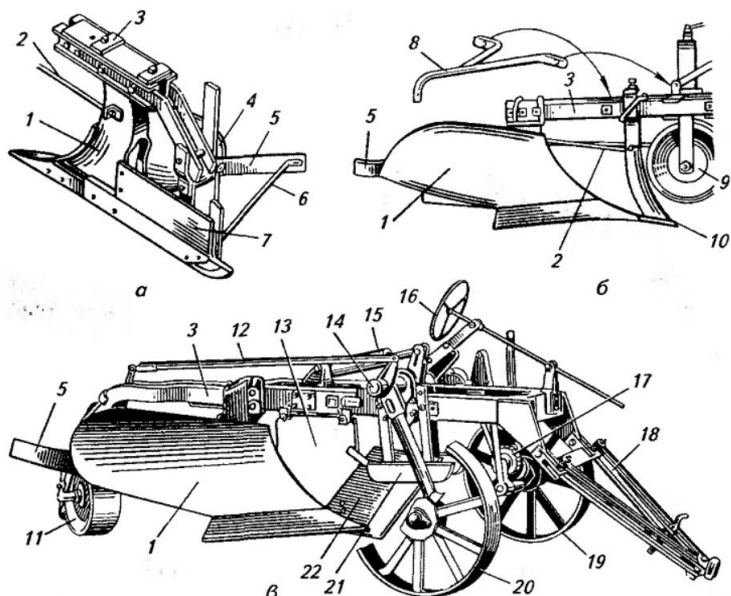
Кустарниково-болотные плуги: а — корпус плуга; б — плуг ПБН-75; в — плуг ПКБ-75; 1 — корпус; 2, 6 — раскосы; 3 — рама; 4 — отвал; 5 — перо; 7 — уширитель; 8 — кустоукладчик; 9, 11, 19, 20 — колеса; 10, 22 — ножи; 12 — тяга; 13 — щит; 14 — ось; 15 — гидроцилиндр; 16 — штурвал; 17 — автомат; 18 — прицепное устройство; 21 — лыжи
